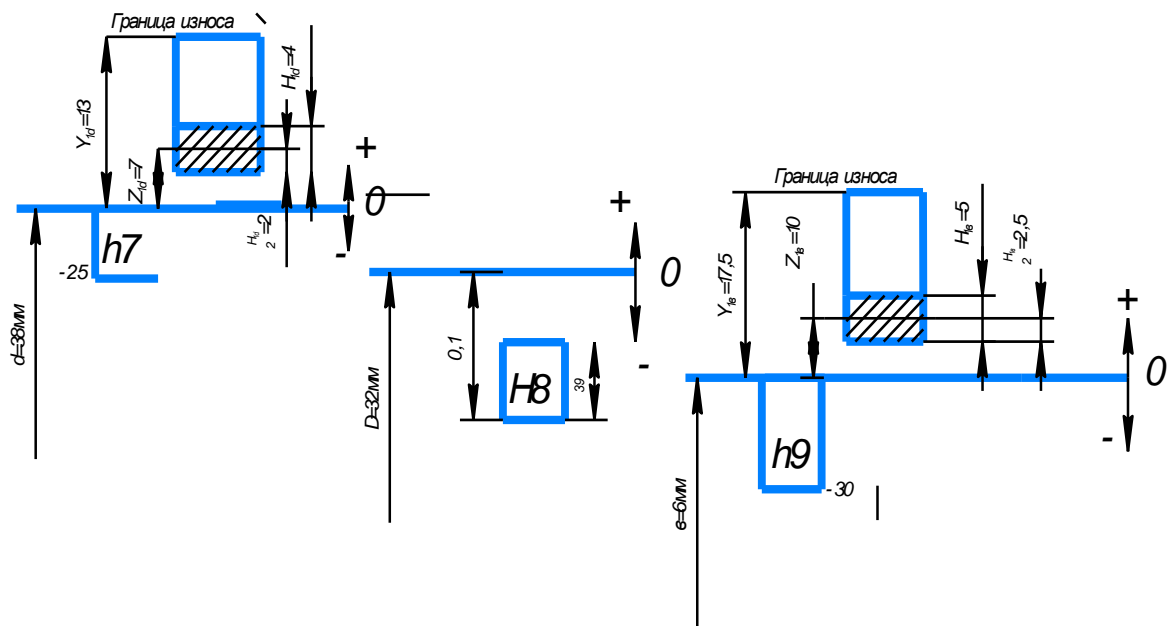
Схема расположения полей допусков калибра- кольца
